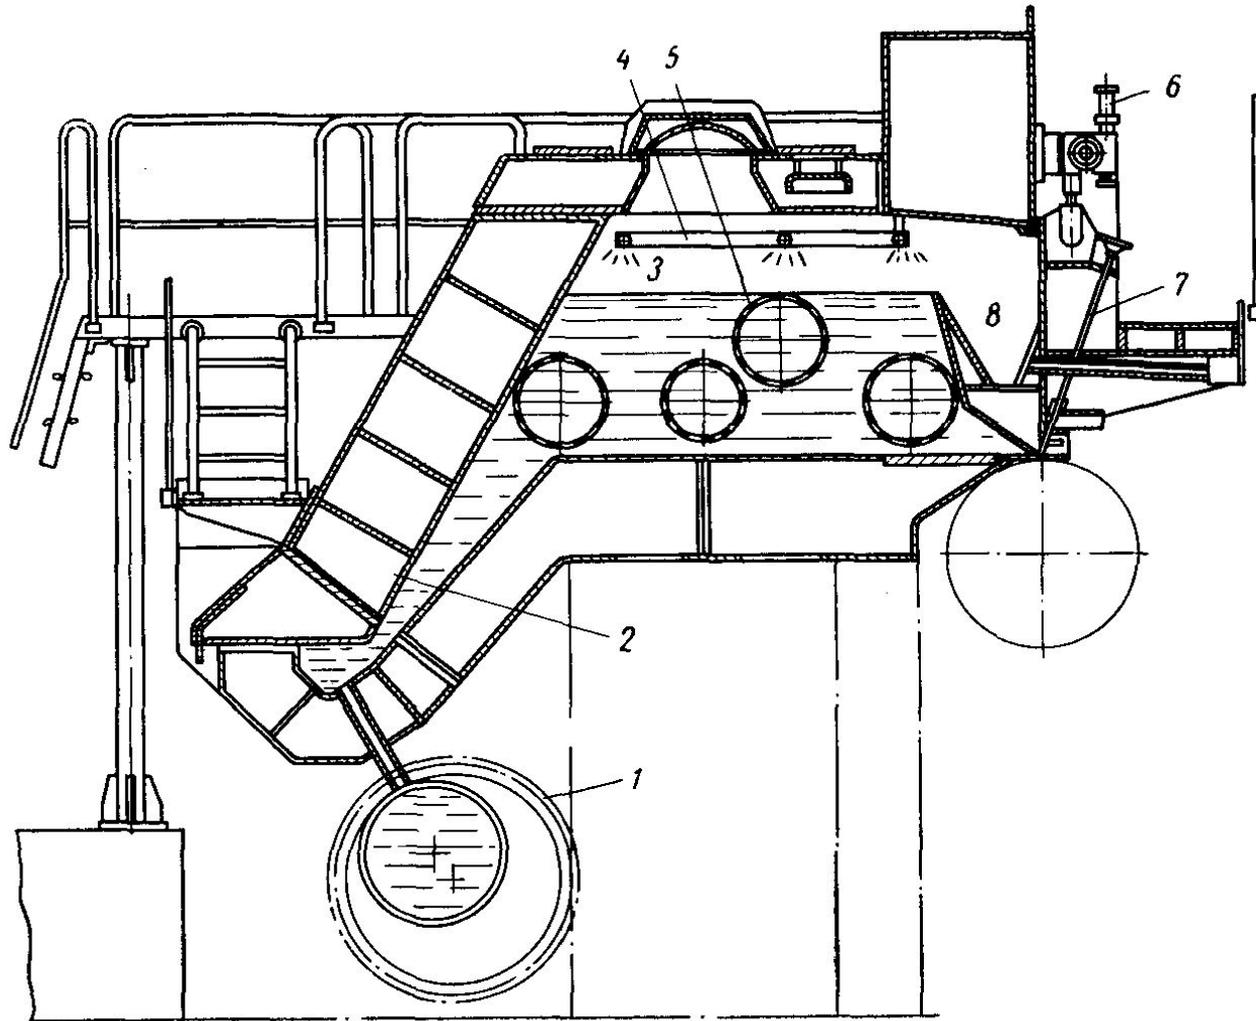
Закрытый напорный ящик с воздушной подушкой:
